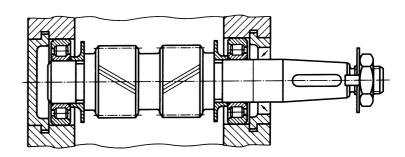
Входной вал шевронной цилиндрической передачи
